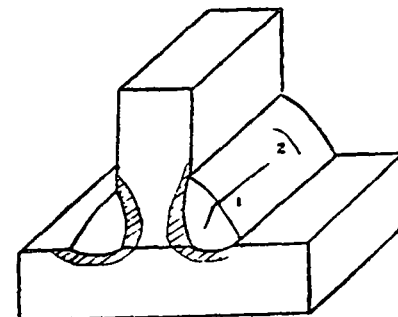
Tipos diversos de grietas en una soldadura en ángulo.
